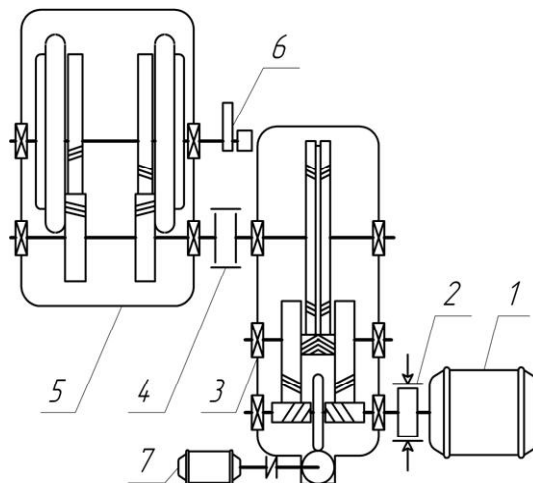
Схема ПГТЭ ЛТ-1, ЛТ-2, ЛТ-3: 1 – главный электродвигатель; 2 – рабочие тормоза; 3 – быстроходный редуктор; 4 – зубчатая муфта; 5 – главный редуктор с тяговыми звездочками и аварийным тормозом; 6 – реле оборотов с приводом; 7 – вспомогательный электродвигатель с редуктором
